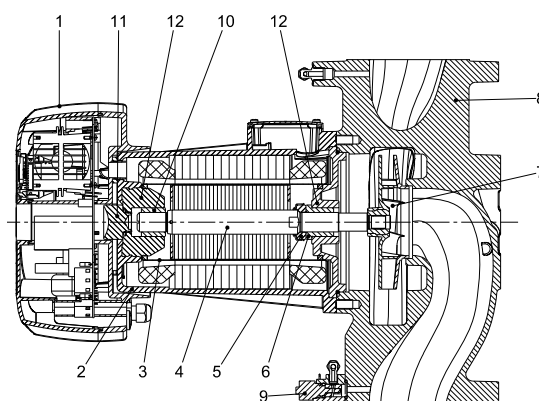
MAGNA 32-120, 40-120, 50-60, 50-120, 65-60, 65-120
